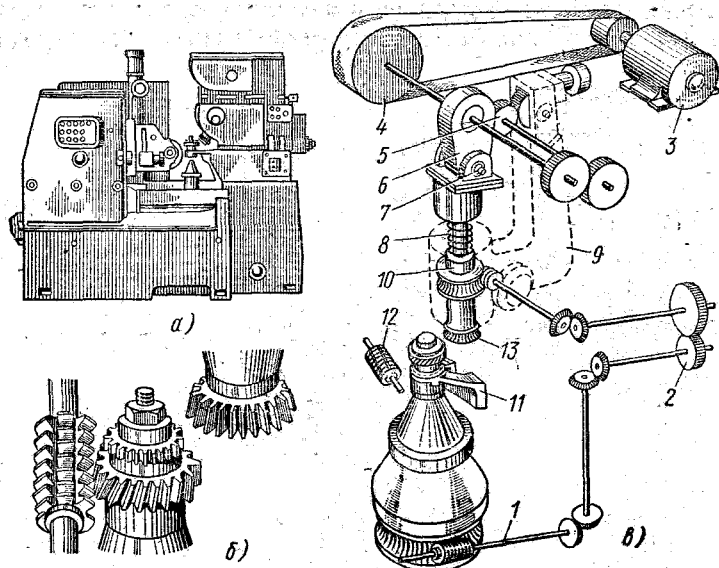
Комбинированный зубофрезерный станок RA-200:
